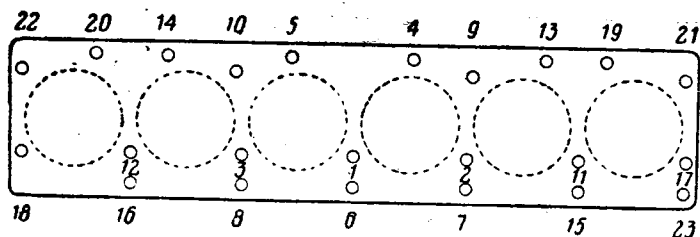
Порядок затяжки болтов головки цилиндров (болты 18 и 22 со стороны радиатора)
